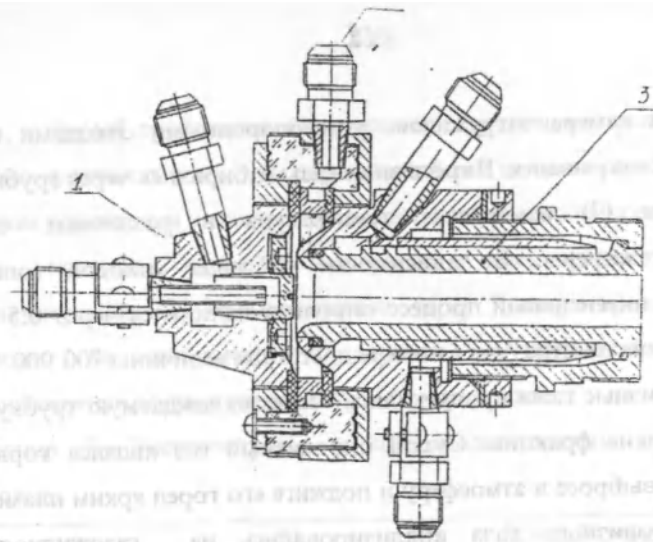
Конструкция дугового плазматрона ПРС-75: 1-катод; 2-вход плазмообразующего газа (воздух); 3-анод.
